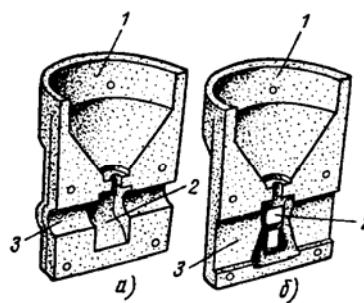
Песчано-смоляные тигель-формы для термитной сварки стальных полос и стержней заземления:
